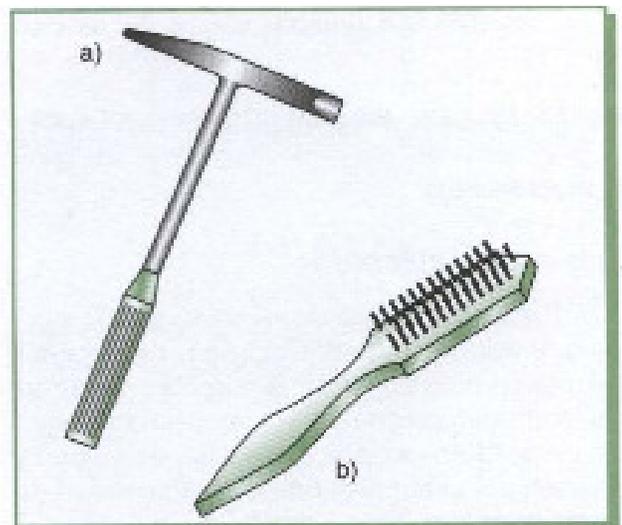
Piqueta y cepillo para la limpieza de la soldadura eléctrica.
